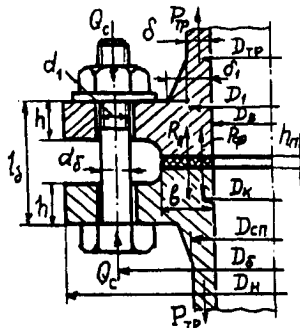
Розрахункова схема з'єднання з безконтактними фланцями
